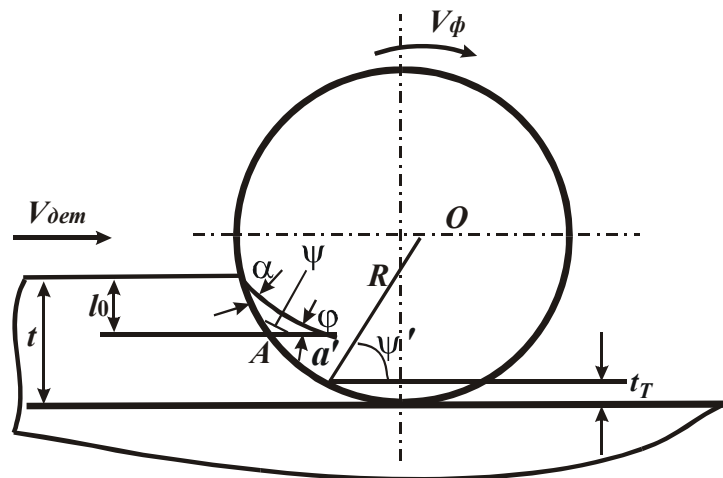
Схема для розрахунку кута α при циліндричному фрезеруванні
